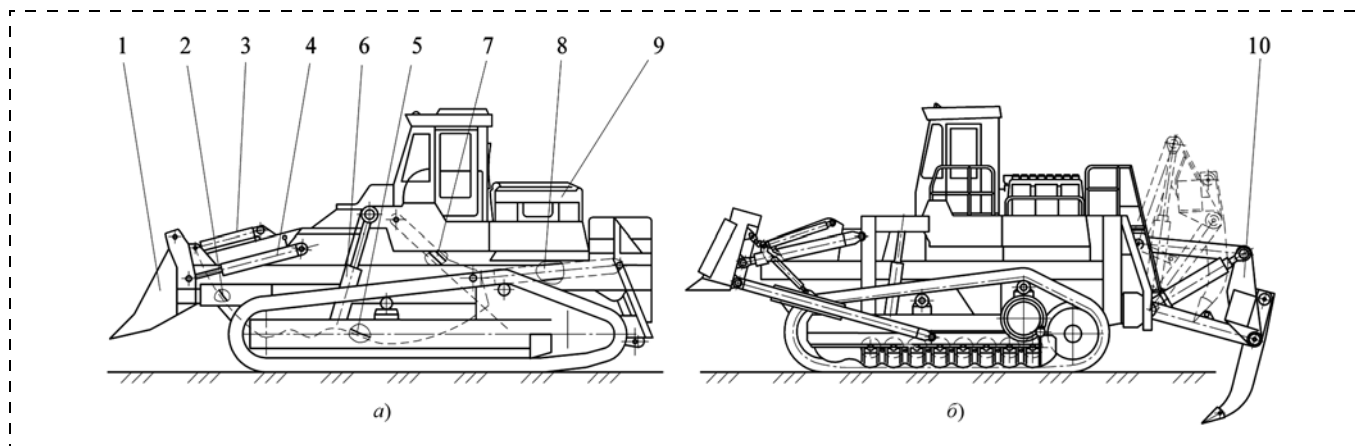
Конструктивные схемы бульдозерно-скреперного агрегата (а) и возможного в перспективе бульдозерно-скреперно-рыхлительного агрегата (б): 1 — отвал; 2 — заслонка; 3 — гидроцилиндр поворота заслонки; 4 — гидроцилиндр поворота отвала; 5 — ковш; 6 — гидроцилиндр подъема-опускания ковша; 7 — поворотная задняя стенка; 8 — гидроцилиндр поворота стенки; 9 — силовая установка; 10 — рыхлительное оборудование
